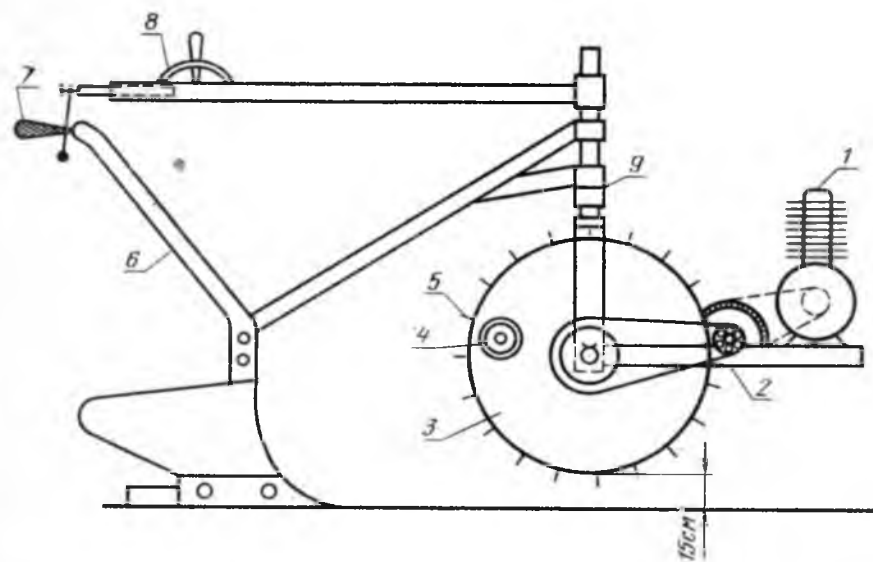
Вид сбоку (без дополнительных колес). 1 — двигатель; 2 — редуктор; 3 — главное колесо; 4 — отверстие с пробкой; 5 — гребни; 6 — конный плуг; 7 — ручка плуга; 8 — рычаг управления газом; 9 — опорное колесо, регулирующее заглубление плуга
